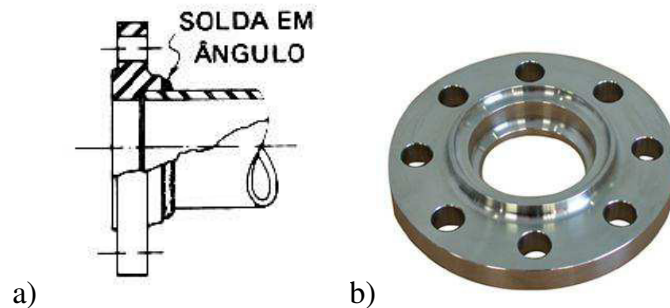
a) Desenho Representativo de um Flange de Encaixe (SENAI, 1997). b) Flange de Encaixe (AHAD Tubeline co., 2012)
